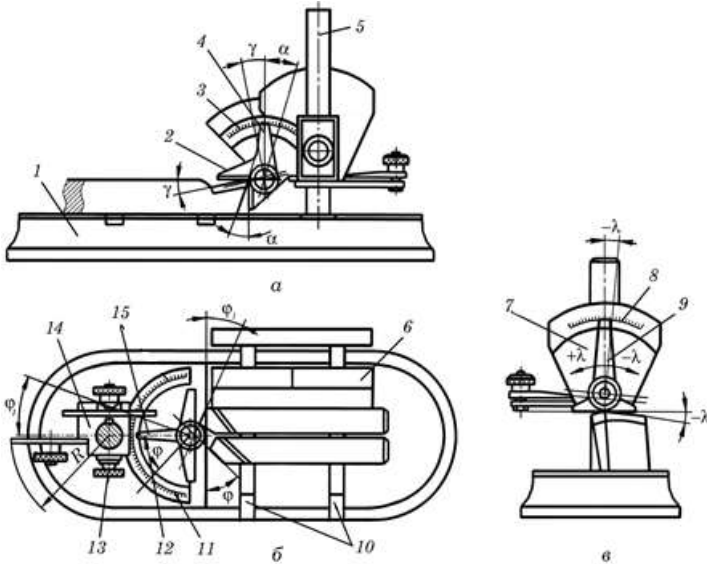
Універсальний кутомір для вимірювання кутів різця:
